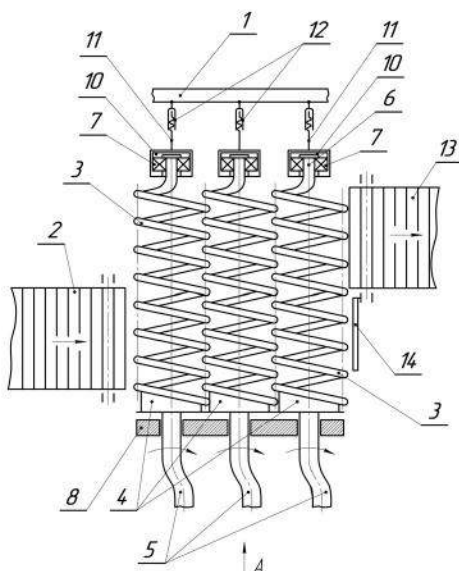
Конструктивна схема нового очисника картопляного вороху
